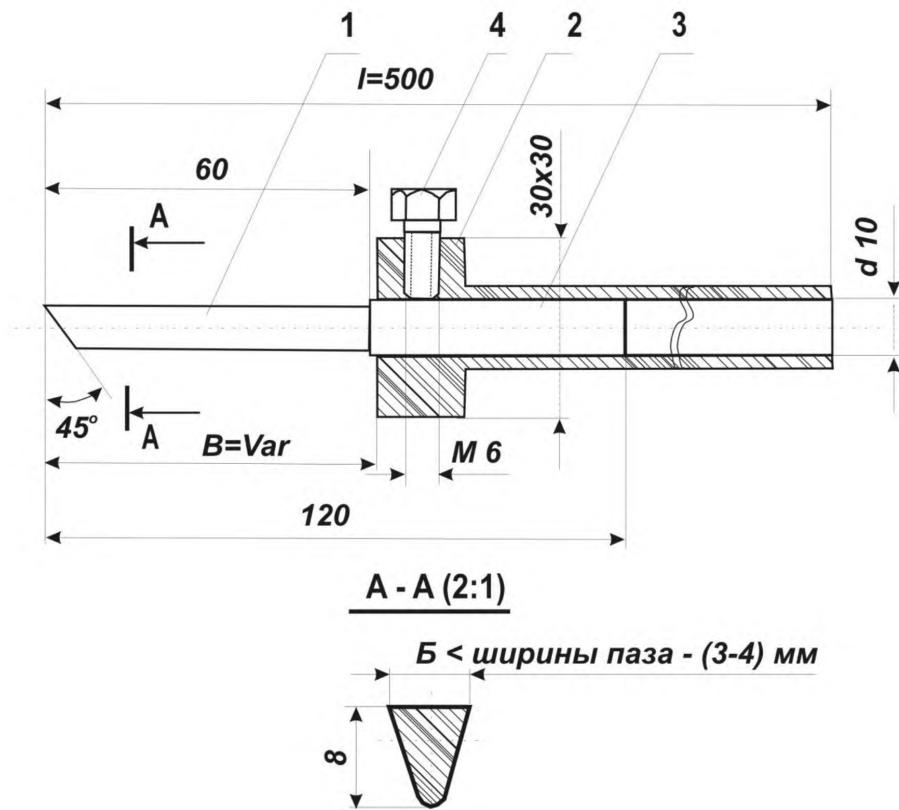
Рычажное устройство для контрольного вырывания мастики из паза шва или камеры трещины:
